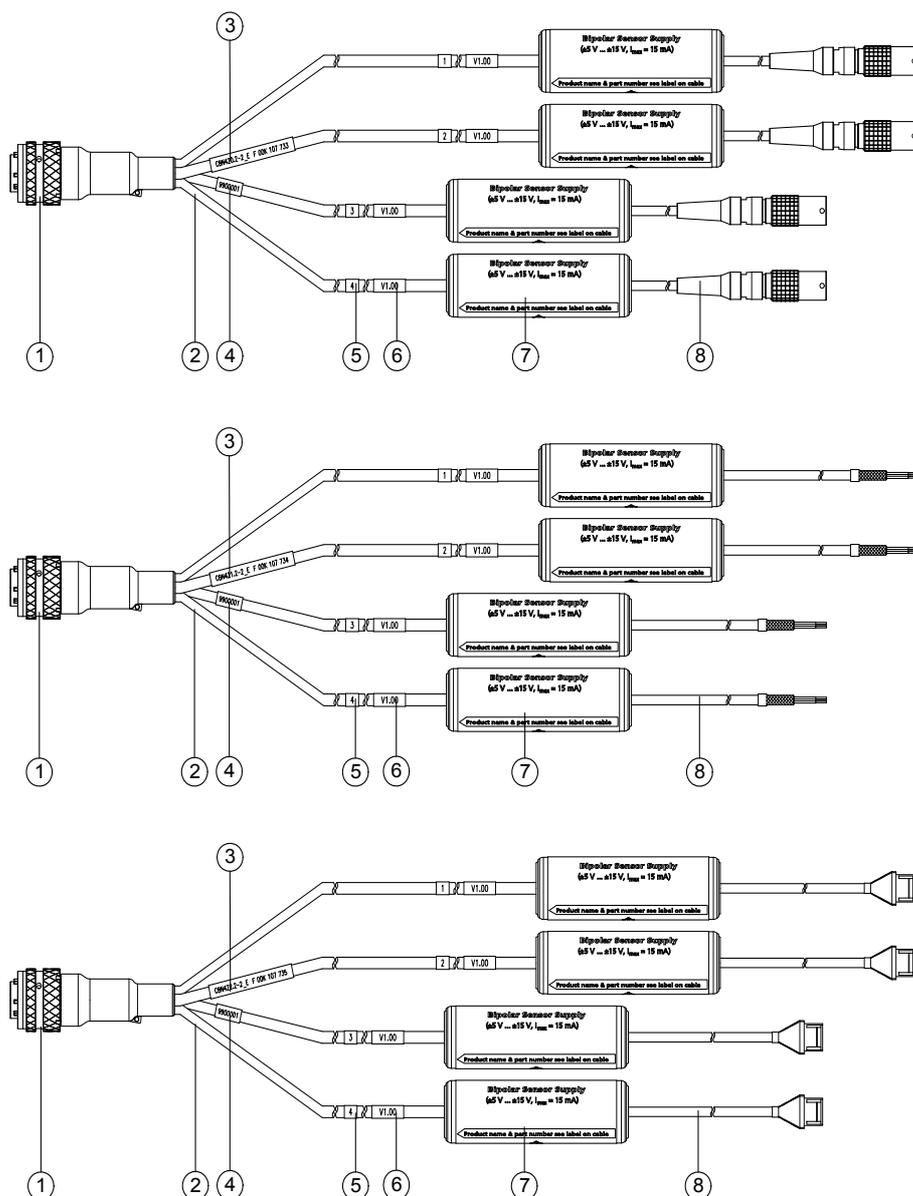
Aufbau des Sensorkabels CBN420.2 (oben, Lemo-Anschluss), CBN421.2 (Mitte, Open Wire) und CBN422.2 (unten, Molex-Anschluss)
